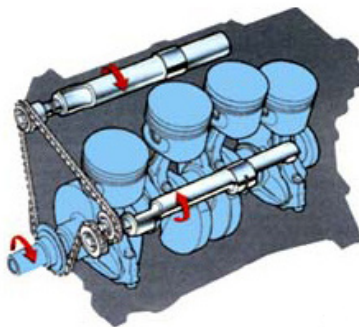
Схема уравнивания двигателя SAAB 2,3 л
